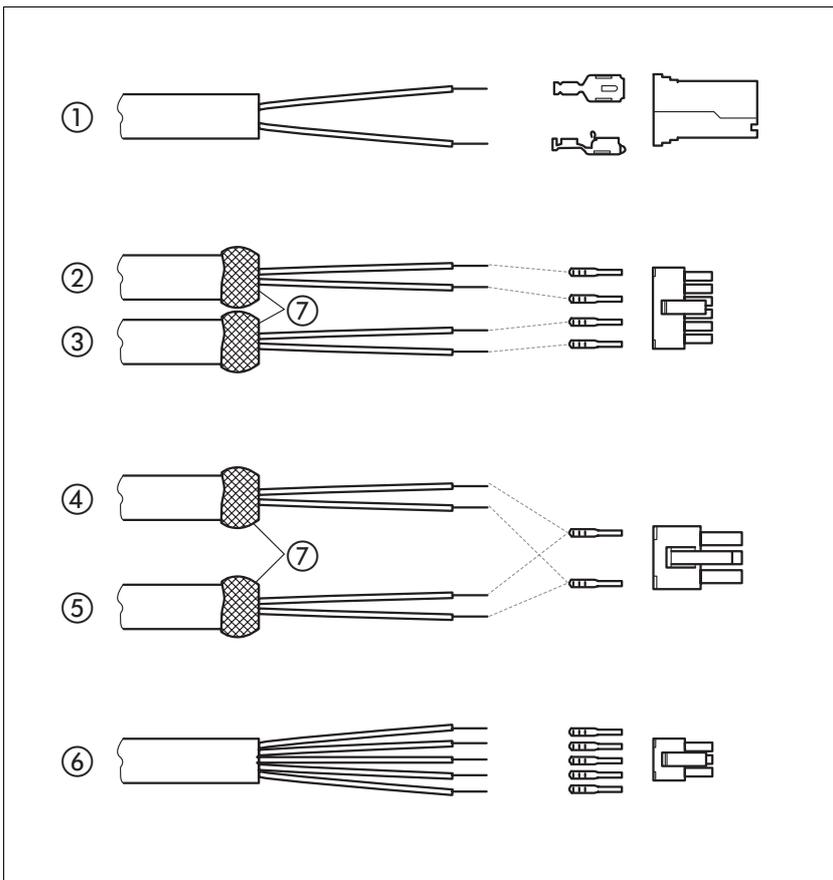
Stecker, Kabelschuhe und Crimpkontakte
